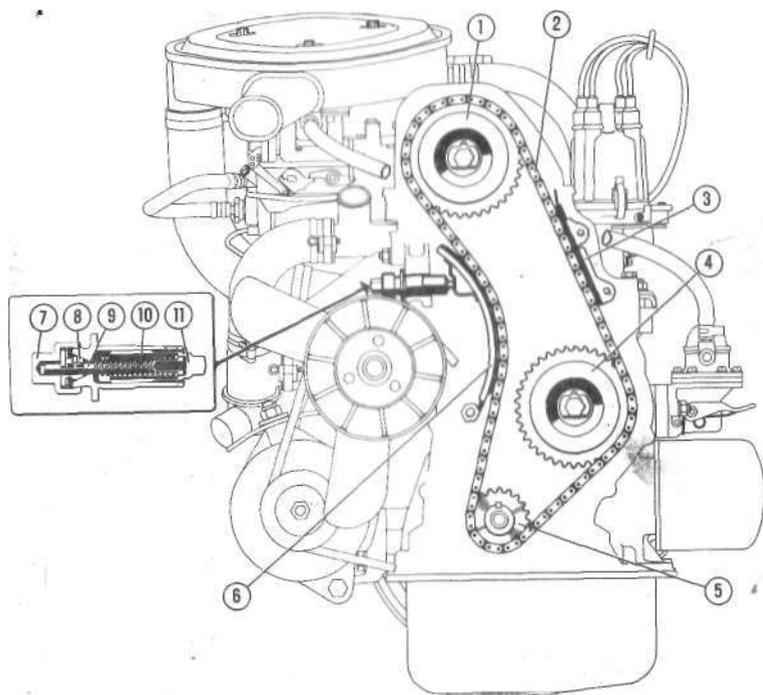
Схема привода механизма газораспределения: 1 — звездочка распределительного вала; 2 — цепь; 3 — успокоитель; 4 — звездочка валика привода масляного насоса; 5 — звездочка коленчатого вала; 6 — башмак натяжителя цепи; 7 — фиксирующая гайка стержня натяжителя; 8 — зажимной сухарь; 9 — регулировочный стержень натяжителя; 10 — пружина; 11 — плунжер натяжителя
